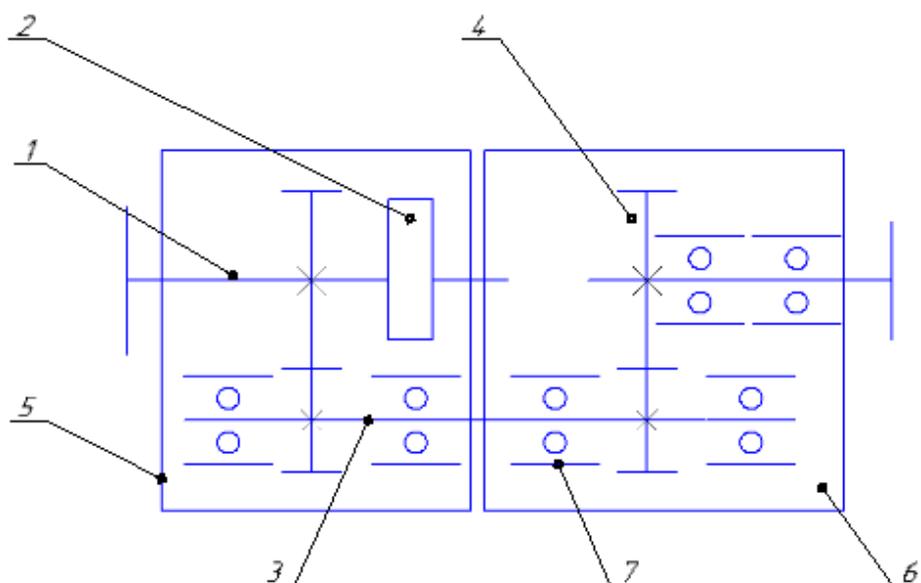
Схема приспособления для шлифования кулачковых валов
